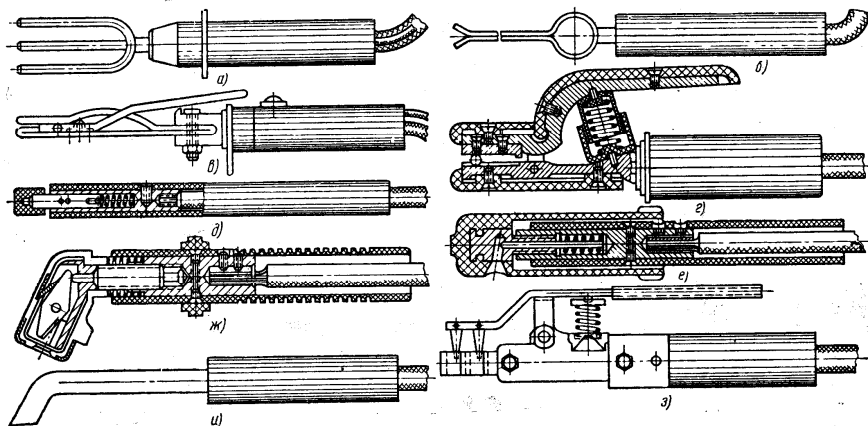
Конструктивные схемы электрододержателей для ручной дуговой сварки:
